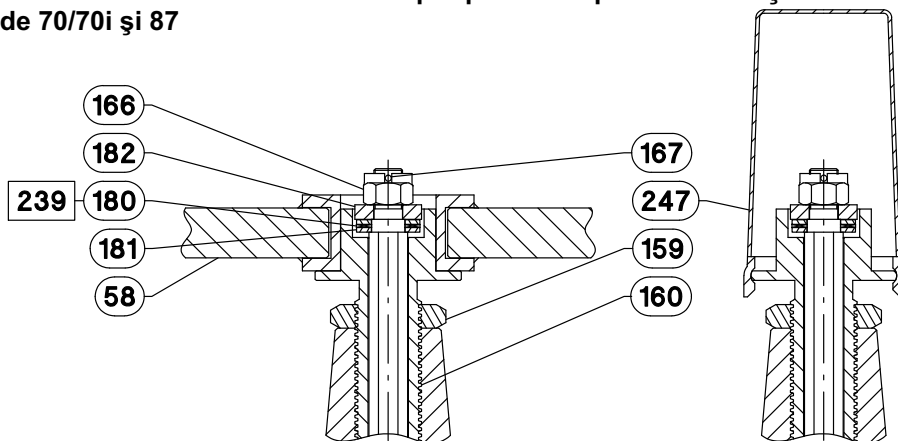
Ansamblul cu roată de mână montată deasupra pentru dispozitive de acționare cu dimensiunea de 70/70i și 87
